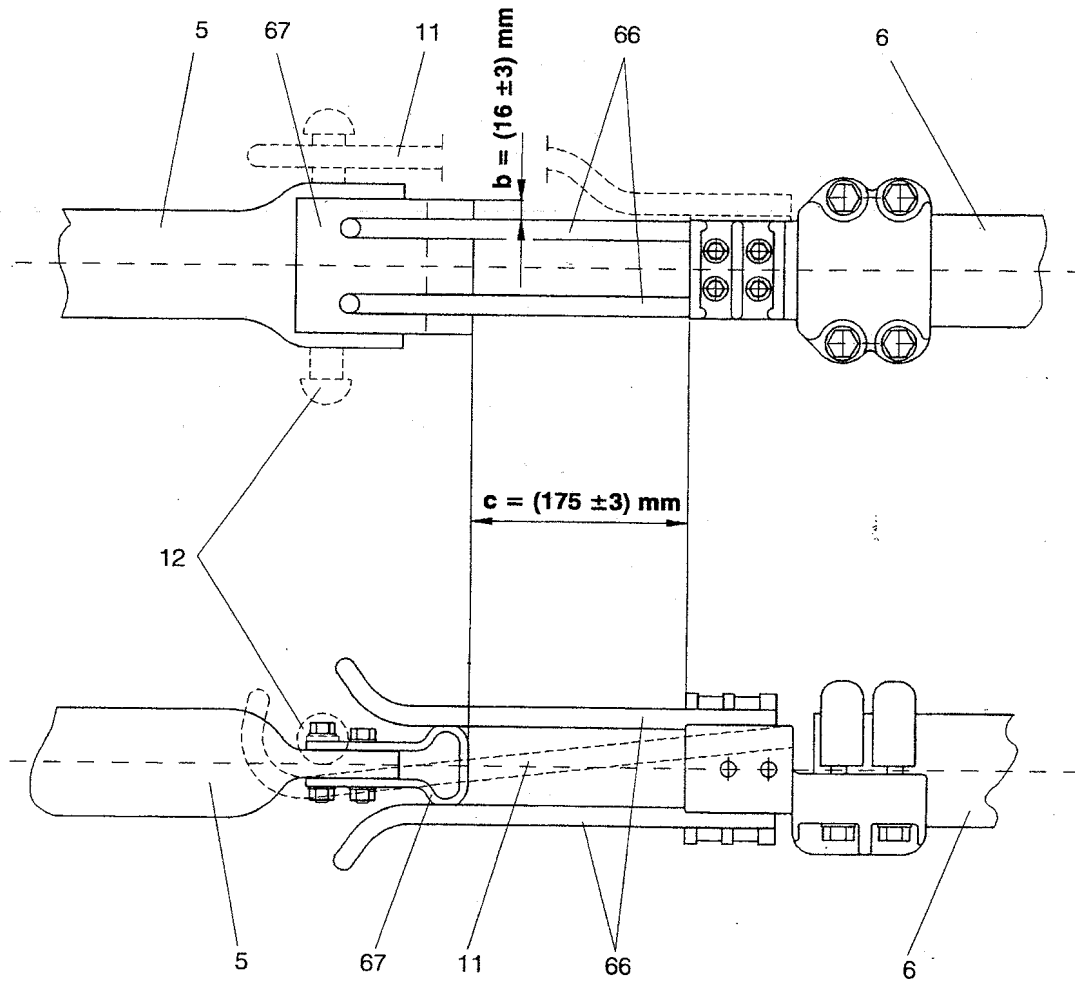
Установка тяг разъединителя: главные контакты разъединителя, регулировка размеров
